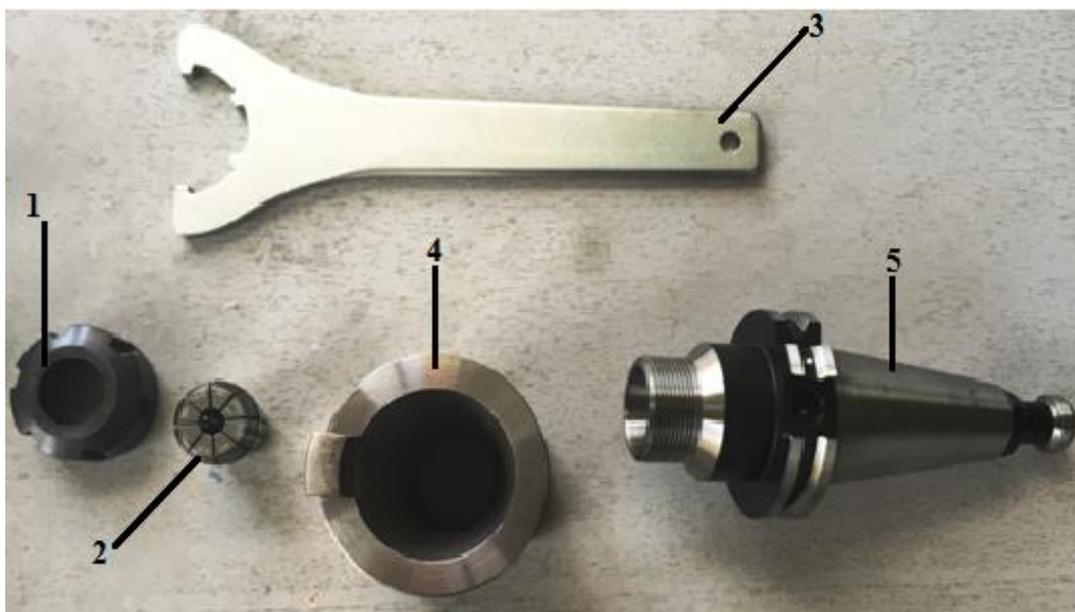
Сборка цангового патрона: 1 - гайка; 2 - цанга ;
